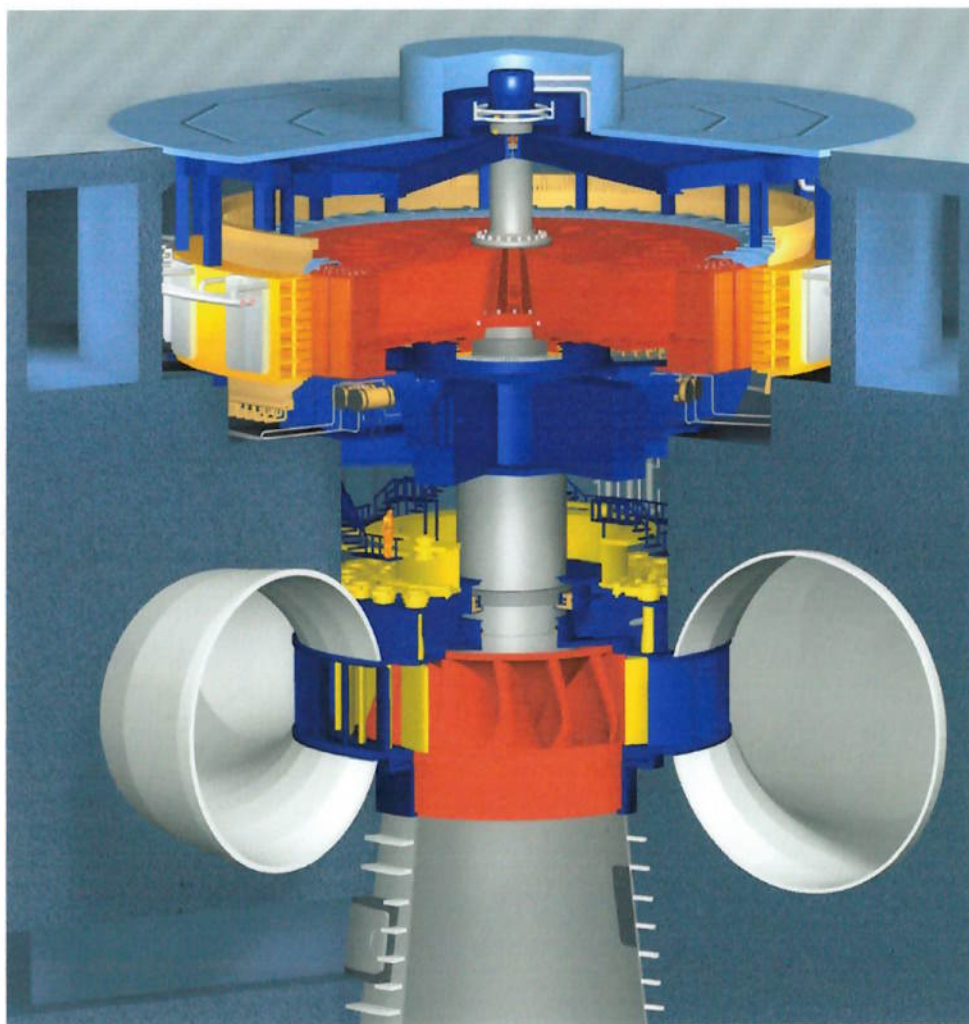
Corte do conjunto Turbina e Gerador de uma usina hidrelétrica
